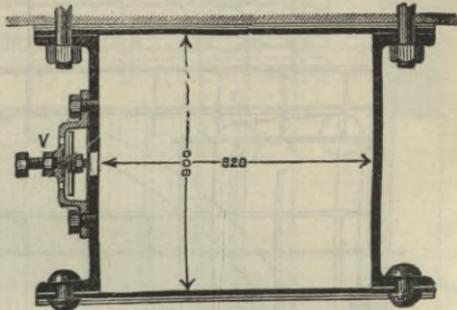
Brems-Apparat f. d. Gegengewicht.
